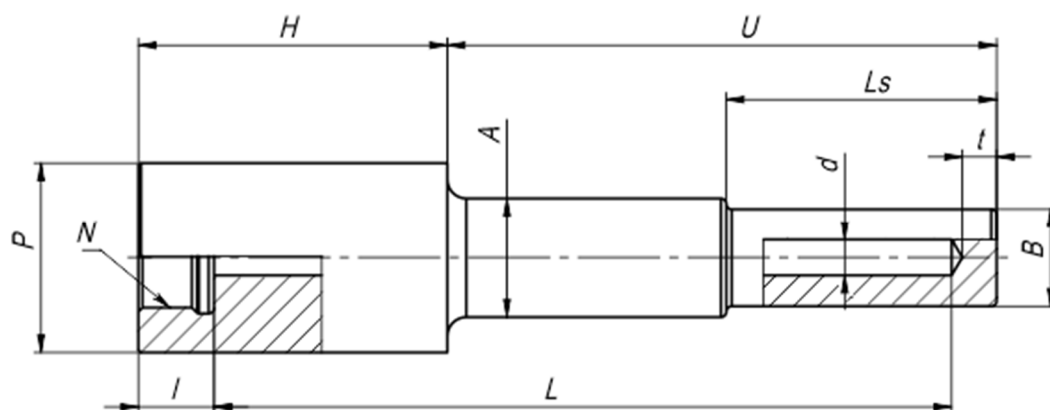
Гильза под приварку через адаптер (Socket Weld), цельноточёная, ступенчатая, под подвижный штуцер.
